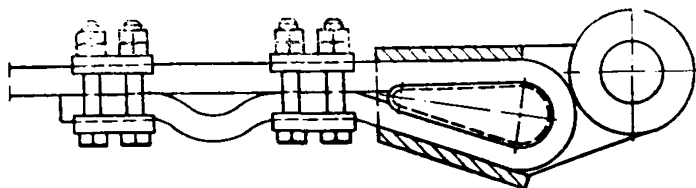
Запанцировка каната в клиновой муфте конструкции ЦНИИподземшахтострой для проходческих подъемных установок
